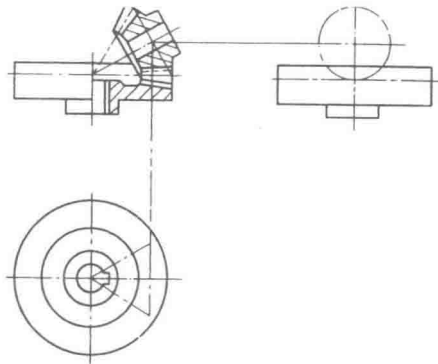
轴线成斜交的平面齿轮与锥齿轮啮合
